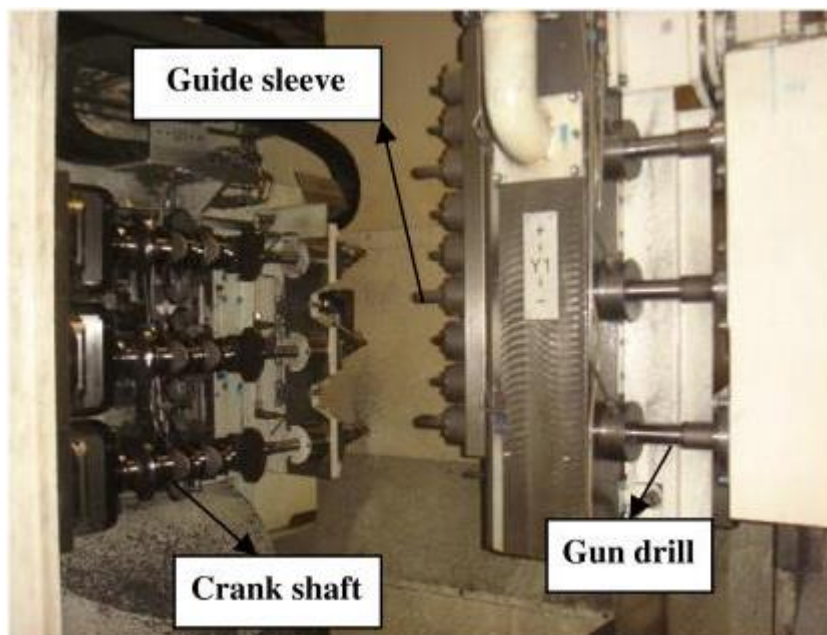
Общий вид зоны обработки станка глубокого сверления мод. BW200-3-800
